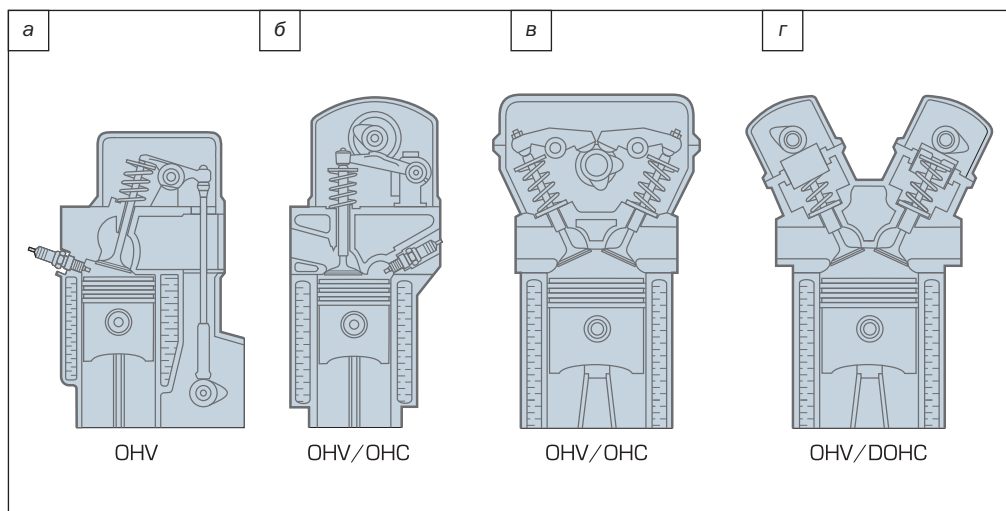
а. Конструктивные варианты привода клапанов: а — привод клапанов с помощью штанг при нижнем расположении распределительного вала; б — привод клапанов рычажным толкателем; в — привод клапанов двумя коромыслами от одного кулачка верхнего распределительного вала; г — непосредственный привод от распределительного вала через толкатель при верхнем расположении клапанов; OHV — верхнеклапанная схема с нижним распределительным валом; OHC — верхнее расположение распределительного вала; DOHC — схема с двумя распределительными валами верхнего расположения
